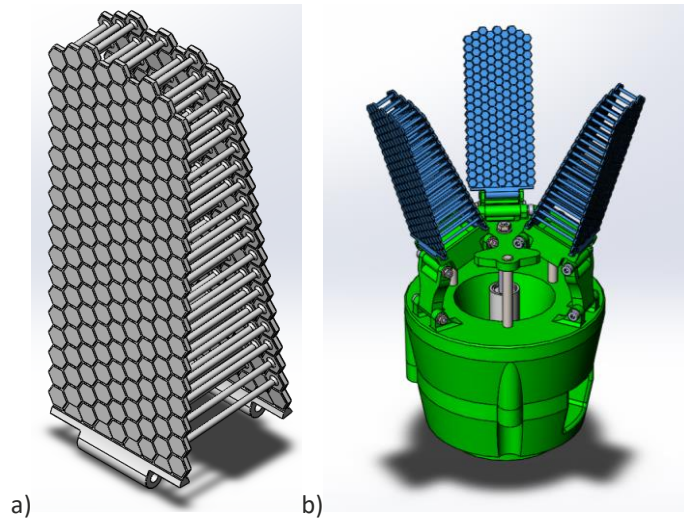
Dedo - vista do componente (a) e montagem no conjunto (b).
